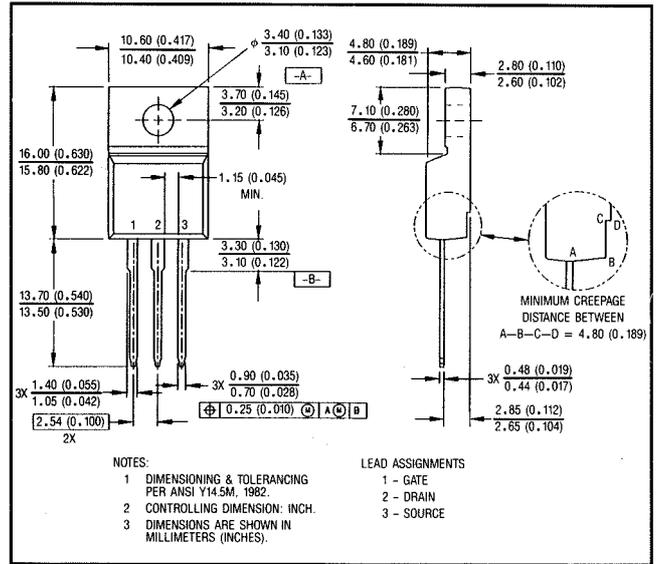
Полностью изолированный пластмассовый корпус Full Pak типа TO-220
